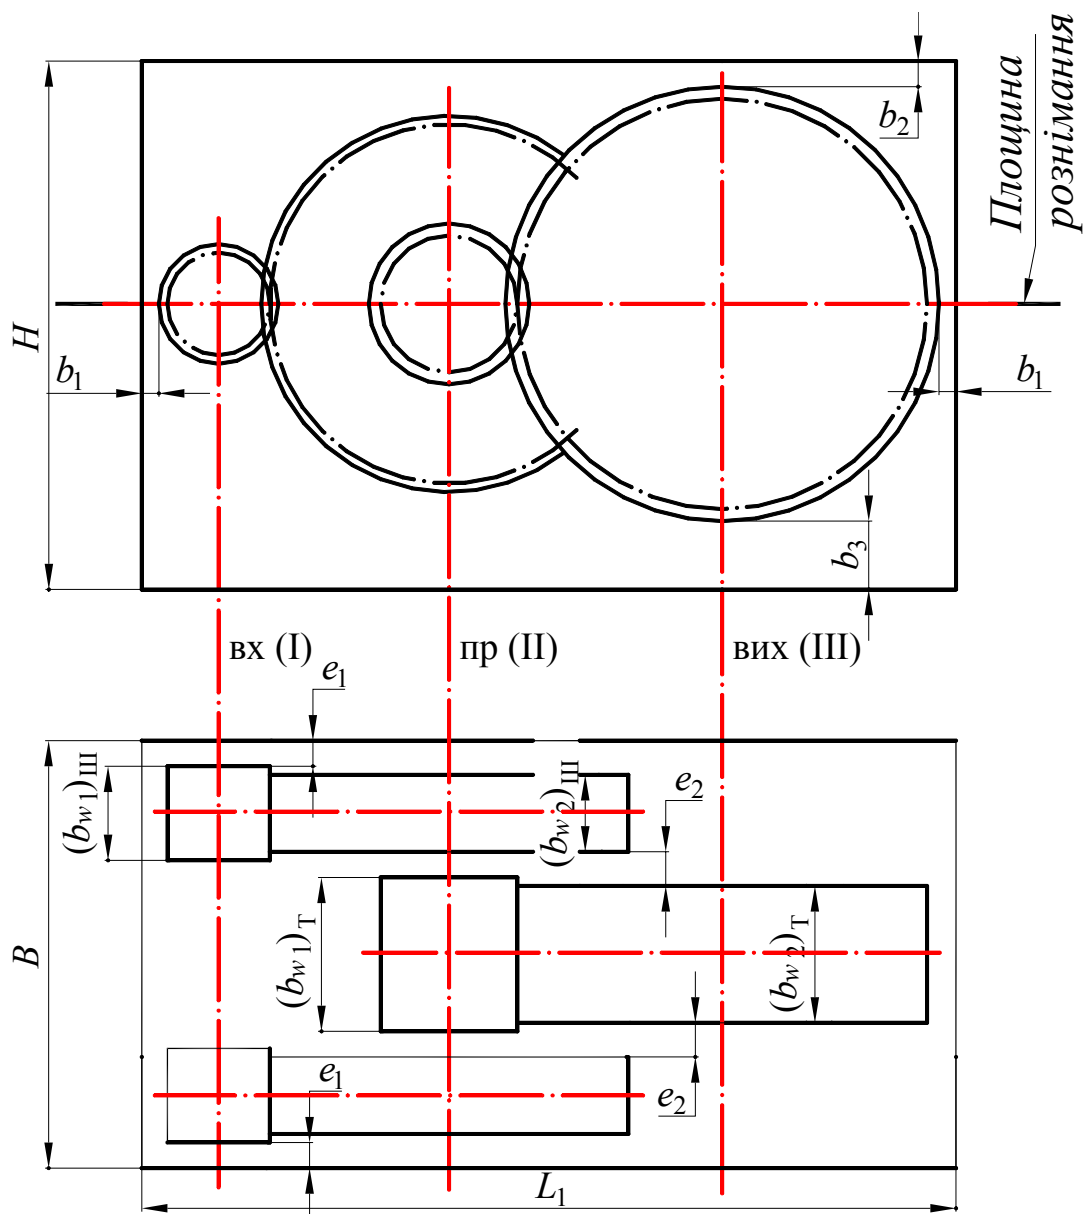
Перший етап ескізного компонування двоступінчастого циліндричного редуктора за схемою роздвоєний шеврон
